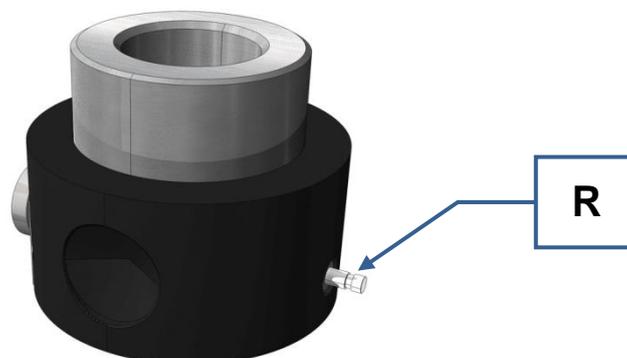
Adapter zur Evakuierung des Presswerkzeuges
